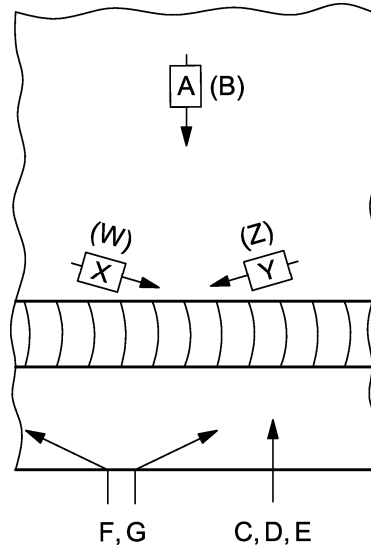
Stumpfschweißnähte in Blechen und Rohren
